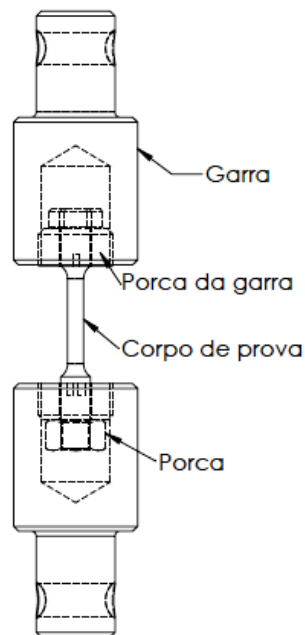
Desenho de conjunto, corpo de prova e garras.
